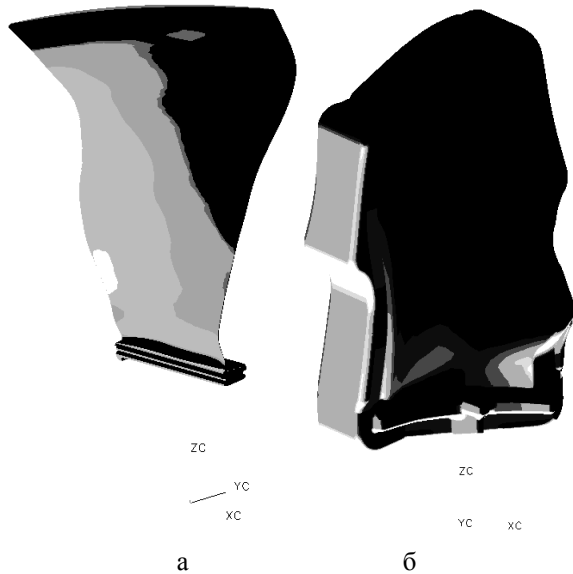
Модель широкохордной вентиляторной лопатки (а) и ее заготовки (б)
